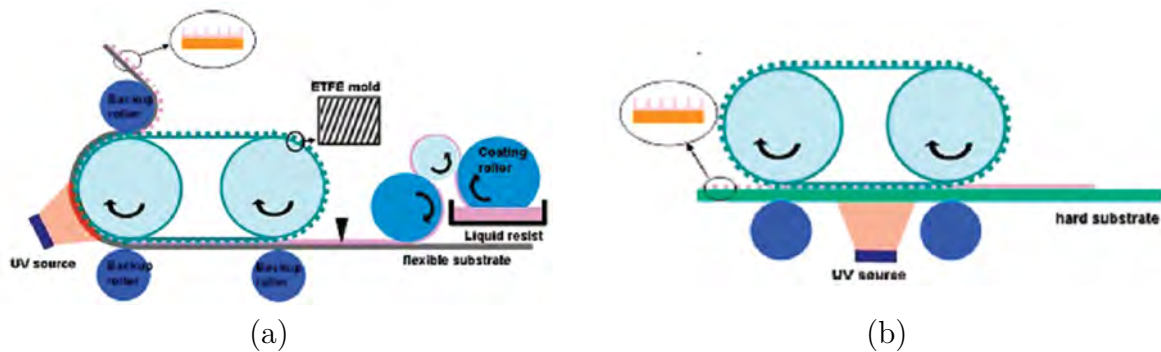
Illustration des procédés de nano-impression sur des surfaces de dimensions non standards : (a) Roll-to-Roll *NIL* (*R2RNIL*) sur un substrat souple, (b) Roll-to-Plate *NIL* (*R2PNIL*) sur un substrat rigide [101].
